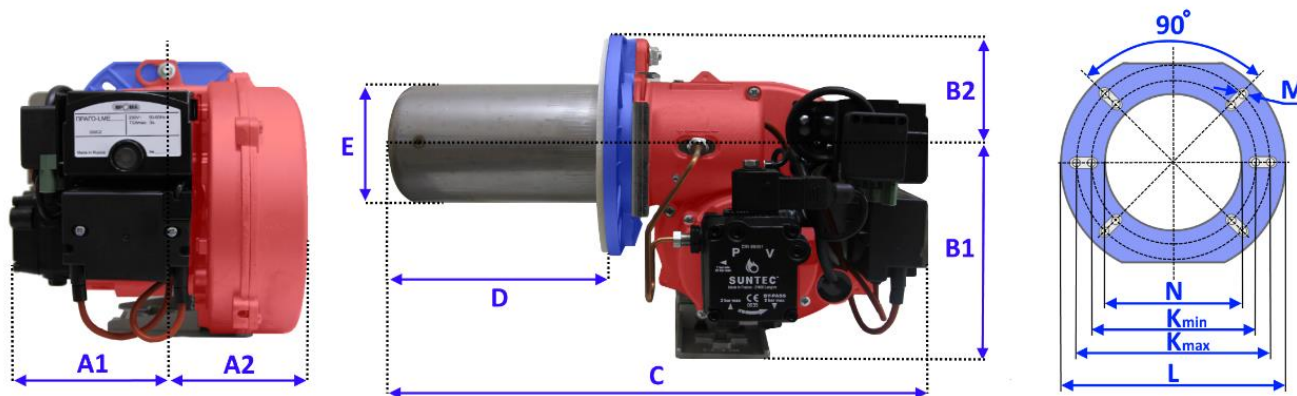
Габаритные размеры горелки ЕММА СО.2-ЛО
